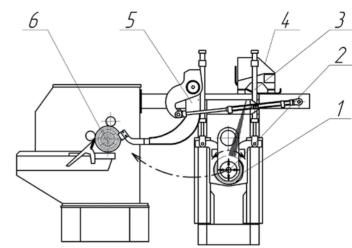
Привод шпинделей ЦЗУ (видны направляющие для перемещения узла по горизонтали) и схема ЦЗУ: 1 — чурак; 2 — шпиндели ЦЗУ; 3 — гидроцилиндры подъема/опускания шпинделей ЦЗУ по вертикали, 4 — балка с ИК-датчиками; 5 — рычажное зажимное устройство; 6 — лущильный станок
